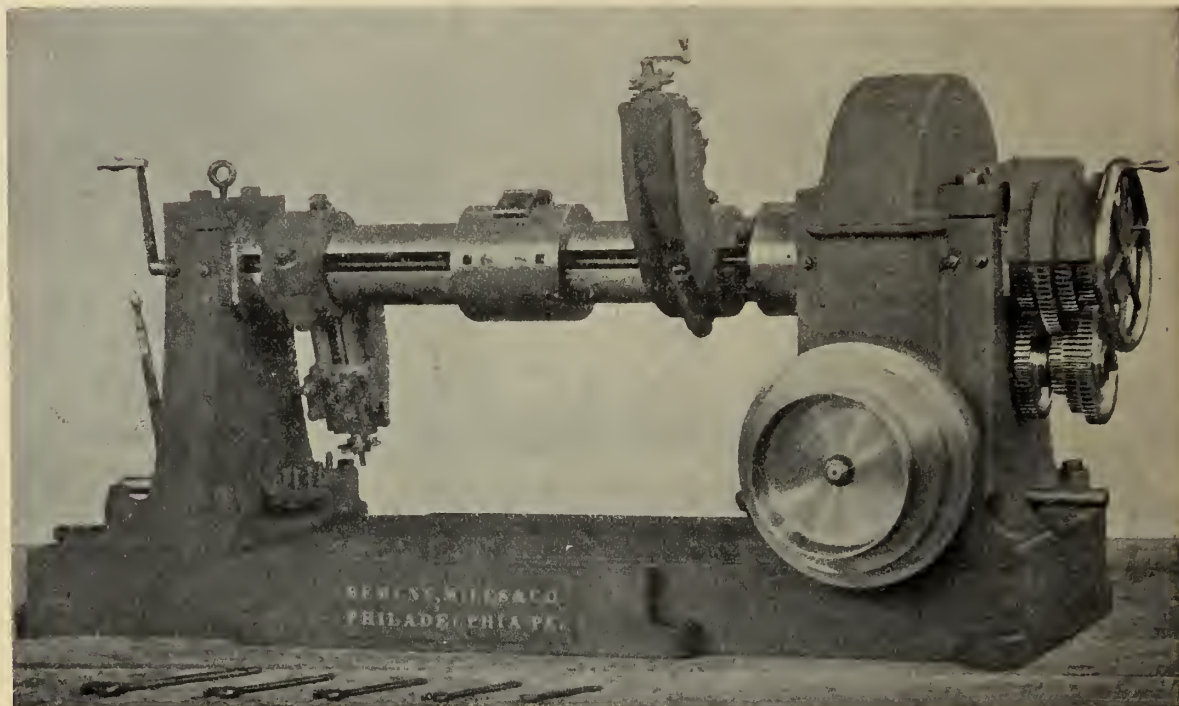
Machine à aléser les cylindres de locomotives type *Bement et Miles*.
